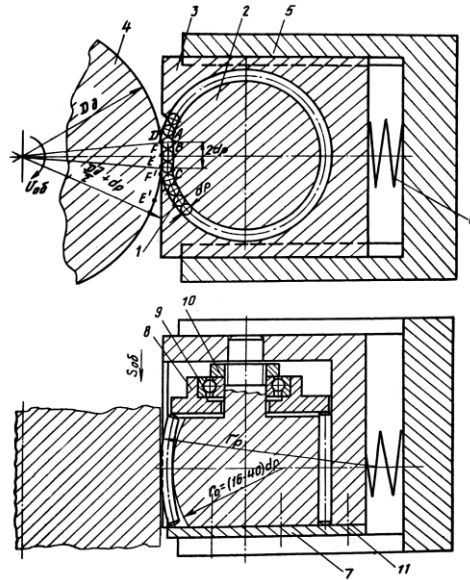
Пристрій для чистової обробки поверхонь тіл обертання оброблюваної деталі. При обертанні деталі із швидкістю $V_{об}$ ролики 1 прокочуються між поверхнями деталі і опукло-увігнутої лиски і деформують поверхневий шар деталі. При цьому ролик, що знаходиться у контакті з облямовуванням і з деталлю відповідно в крапках C і E , деформує поверхню деталі по дузі $E^1E = 2D_p$, а ролик, що знаходиться у контакті з облямовуванням і деталлю в крапках B і E , деформує деталь по дузі $FF^1 = D_p$, довжина дуги: $FE = D_p (D_\partial - D_p) / D_\partial$.
